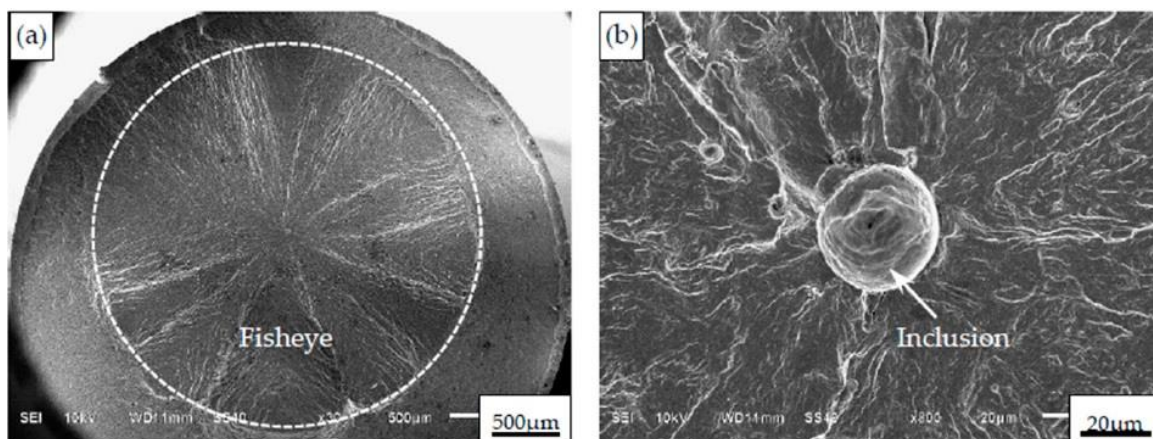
Внешний вид поверхности излома с трещиной типа «рыбий глаз» в стали.
